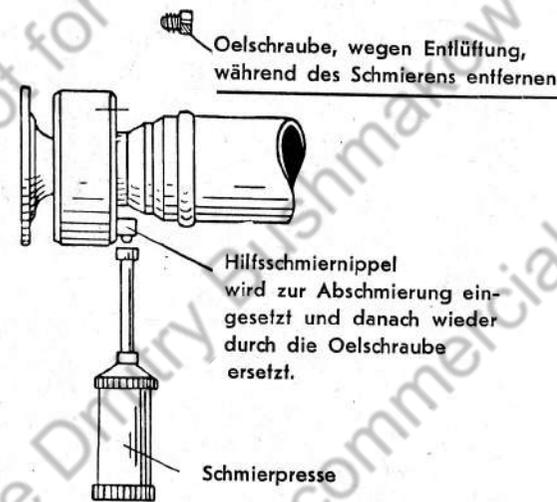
Abschmieren der Kugelgelenke mit Schmiernippel.
